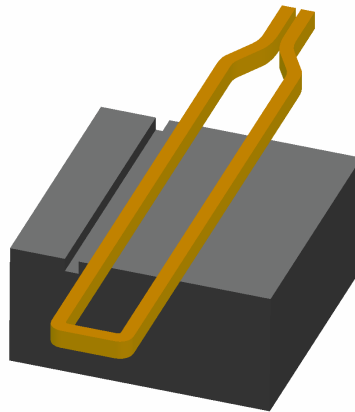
Versuchswerkzeug mit externem Induktor [5]
